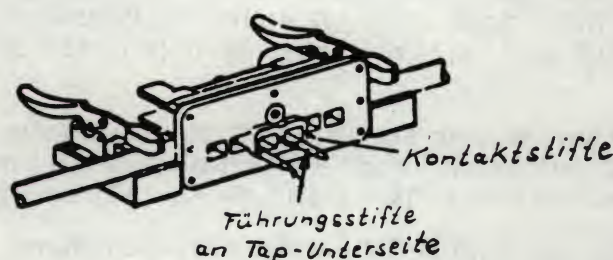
Anschluss-Tap mit angelegter Bohrvorrichtung
